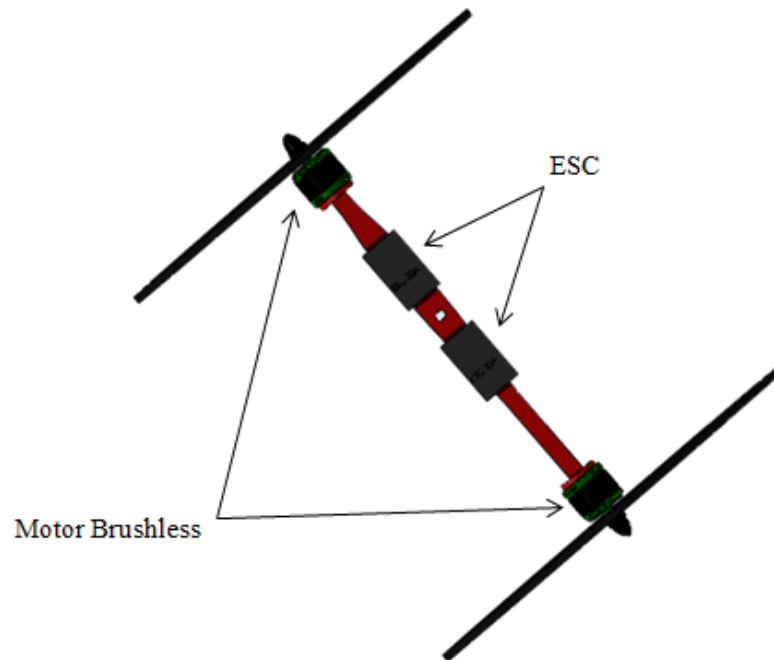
Rotor coaxial frontal (R_1 ou R_2).
